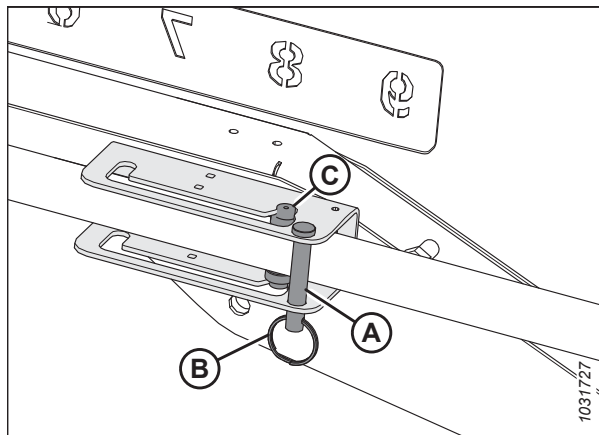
Réglage des vérins avant-arrière de type 2 – Position arrière
